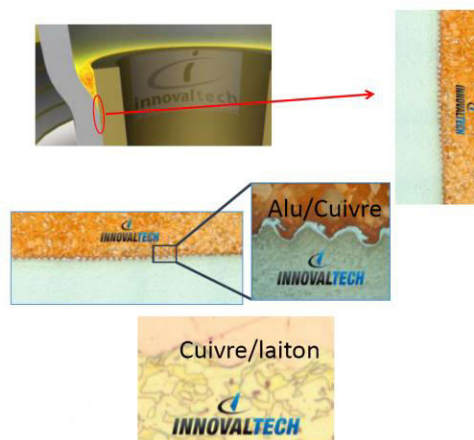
Géométrie microscopique de la soudure par Impulsion Magnétique
